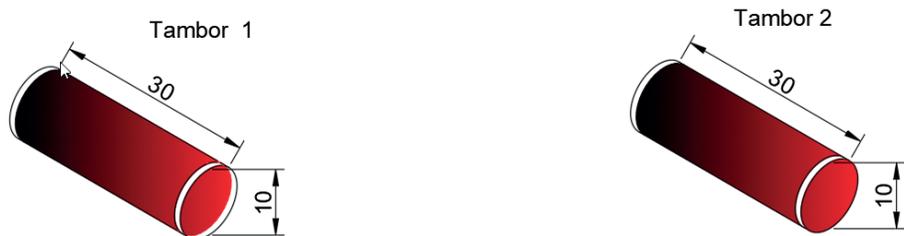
Tambores ou rodillos de la máquina peladora de habas.
